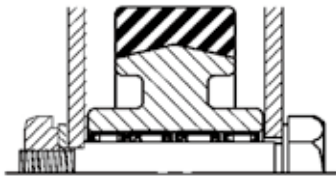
Freilauf mit Lagerung für hohe Belastung
